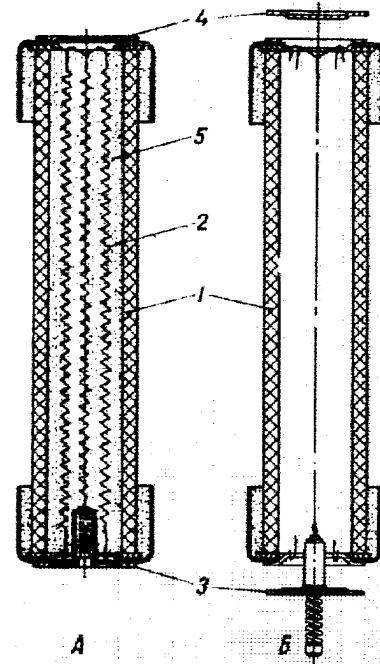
Патрон предохранителя со спиральными плавкими проволоками:
